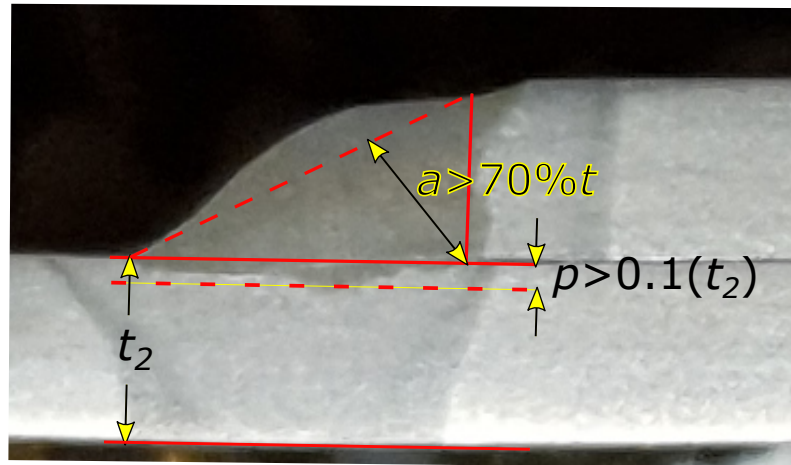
Sección transversal del cordón de soldadura que muestra las condiciones para el límite inferior de calidad.
